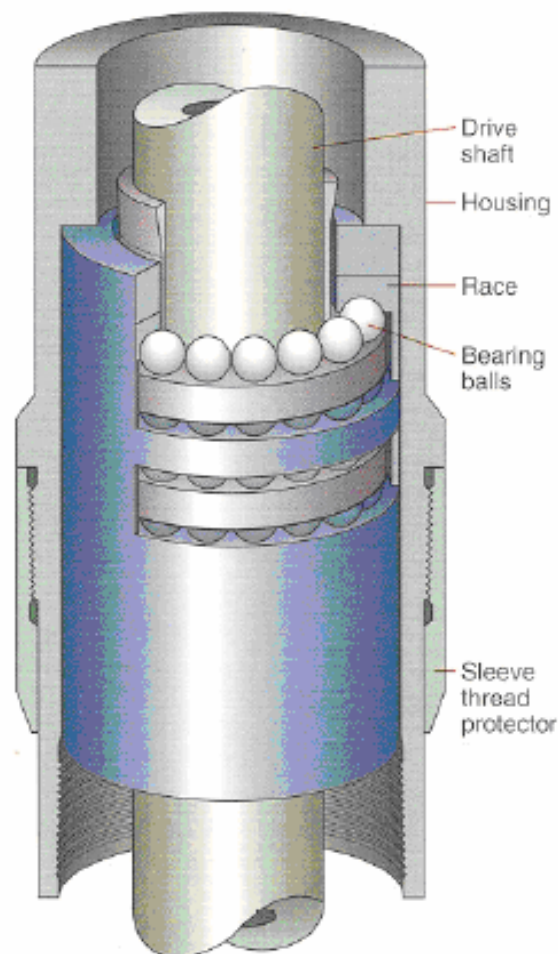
Ensamble del Cojinete con el Motor de Desplazamiento Positivo.<sup>2</sup>
